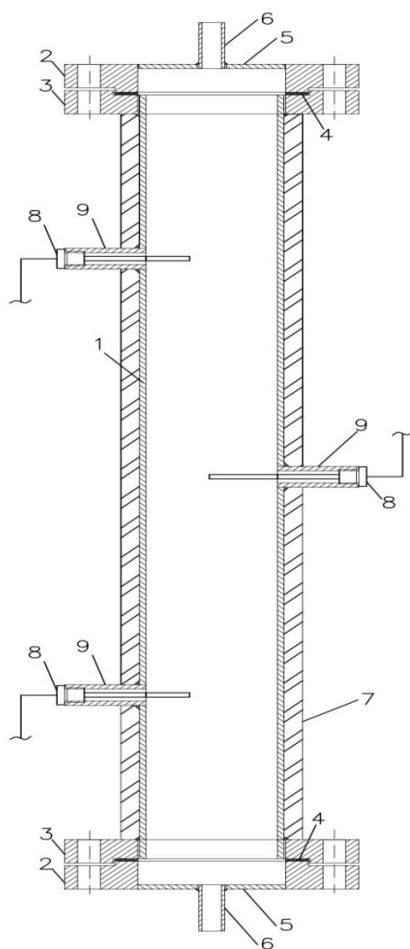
Пиролизёр проточного типа с неподвижным слоем: 1 – труба из нержавеющей стали; 2 – фланец с «выступом»; 3 – фланец с «впадиной»; 4 – прокладка; 5 – вставка в фланец; 6 – трубка; 7 – нагреватель и изоляционный материал; 8 – термопреобразователь; 9 – бобышка для термопреобразователя
